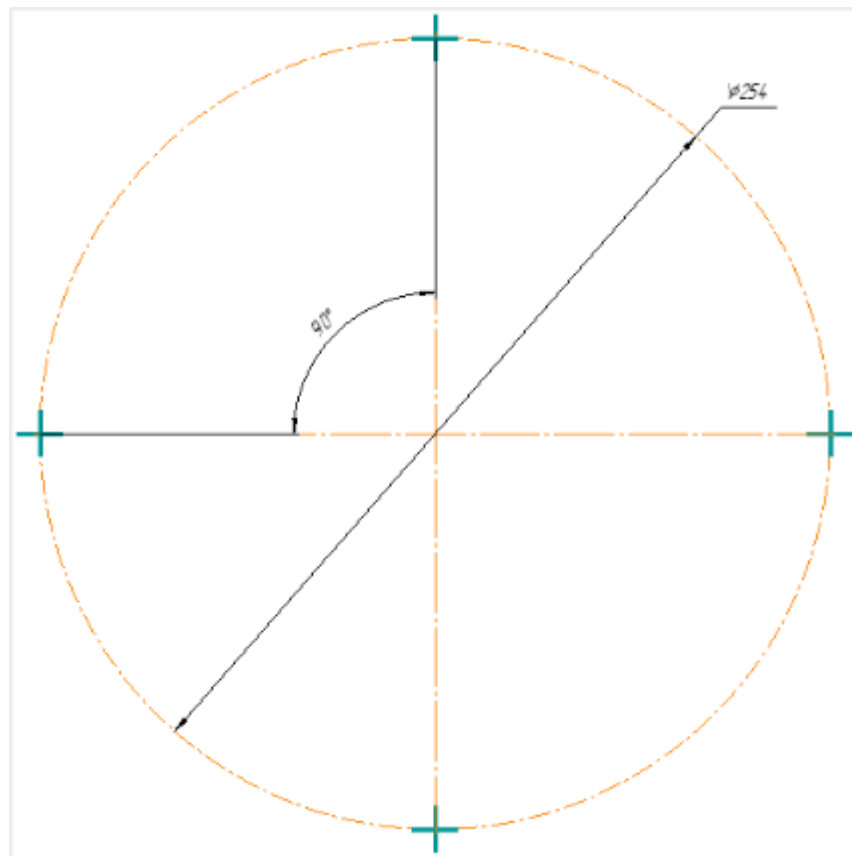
Схема разметки отверстий для монтажа манипулятора
